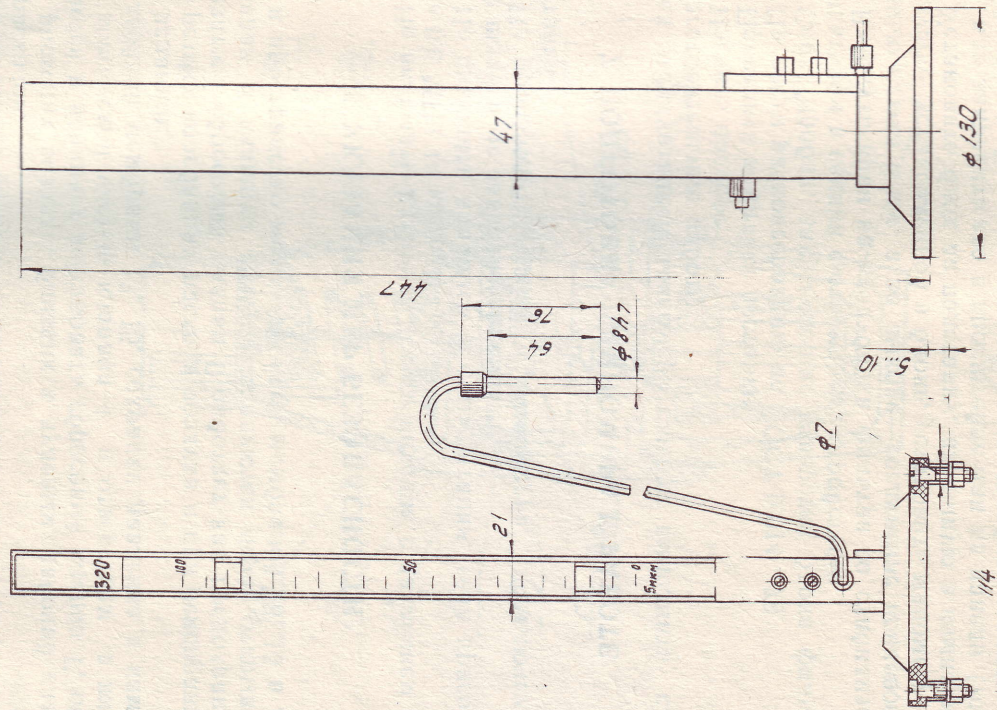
Габаритные и присоединительные размеры прибора (без блока фильтра со стабилизатором).
